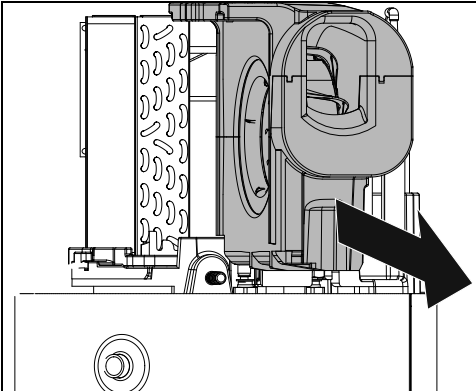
Baugruppe Luftführung und Gebläse entfernen
